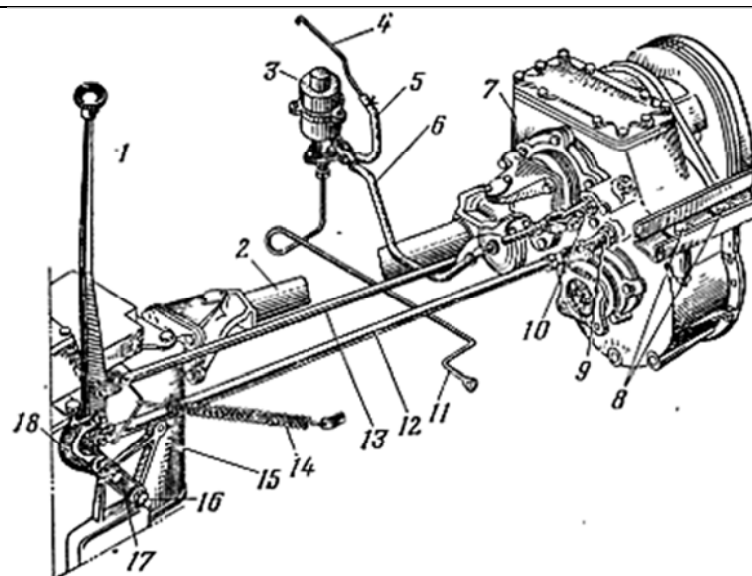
Привод управления раздаточной коробкой автомобиля ЗИЛ-131:
